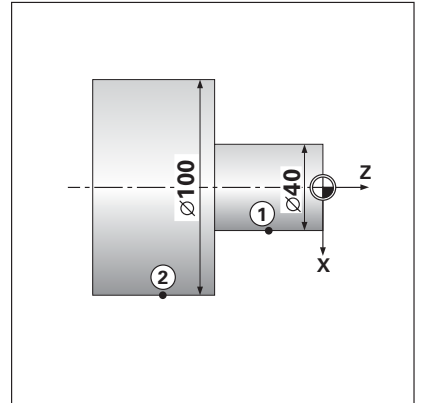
Werkstück-Zeichnung zum Beispiel „Aufmaße“; Werkzeug-Positionen ohne Auf- oder Untermaß
